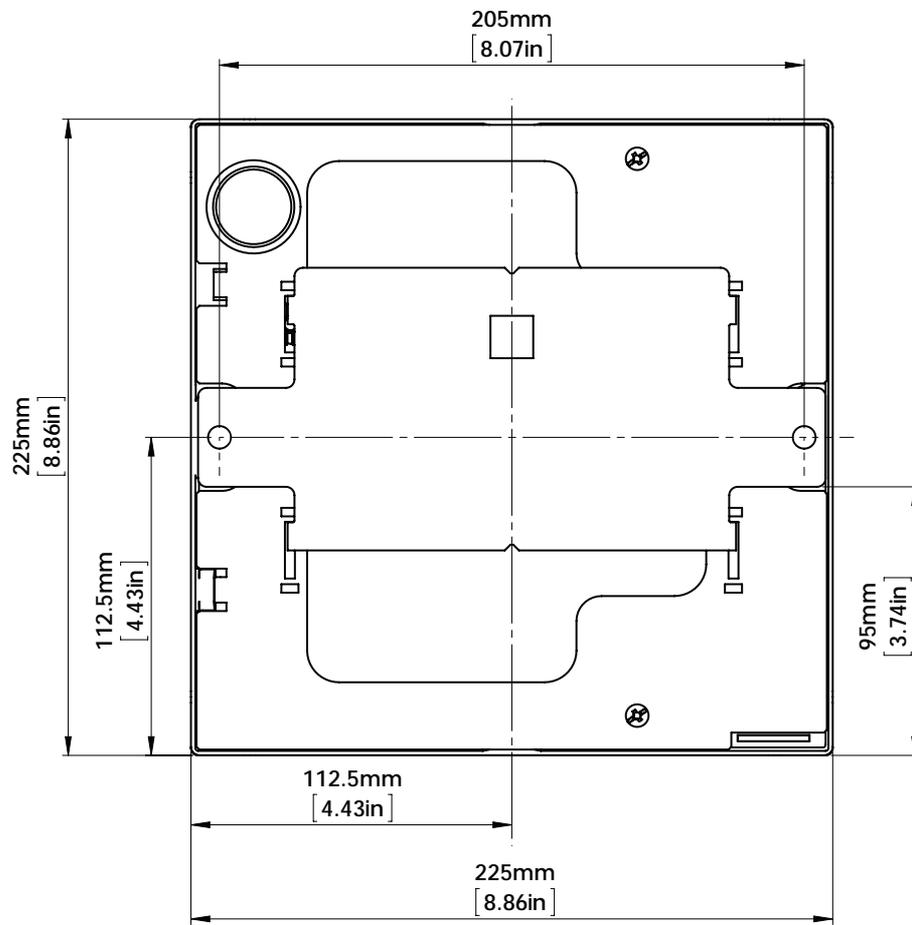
Rilevatore XCC dimensioni - vista posteriore
